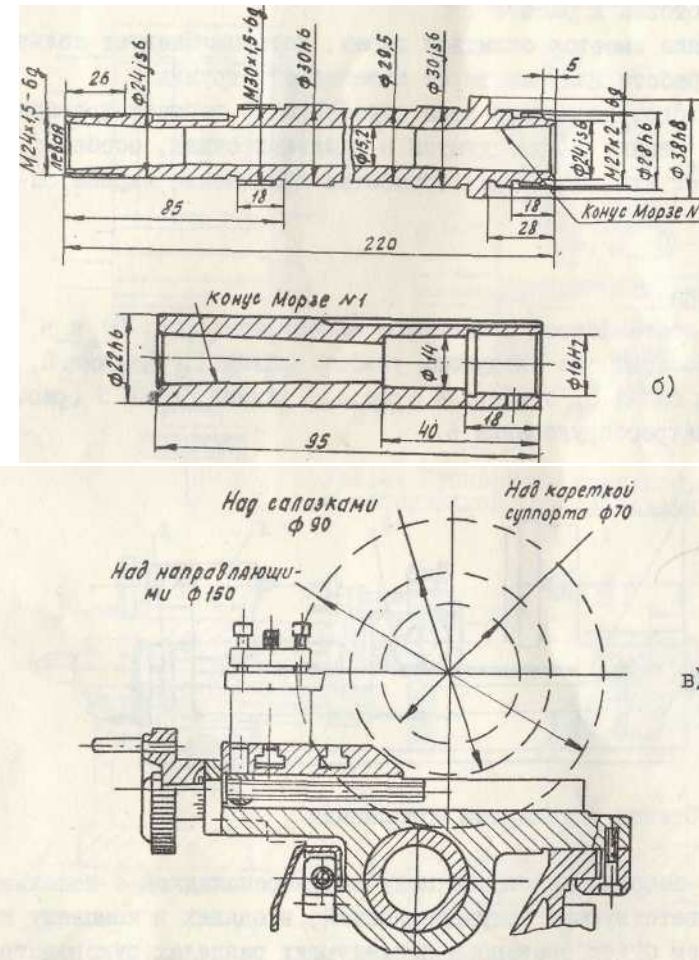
Базовые и присоединительные размеры шпинделя (а), пиноли (б) и суппорта (в)
